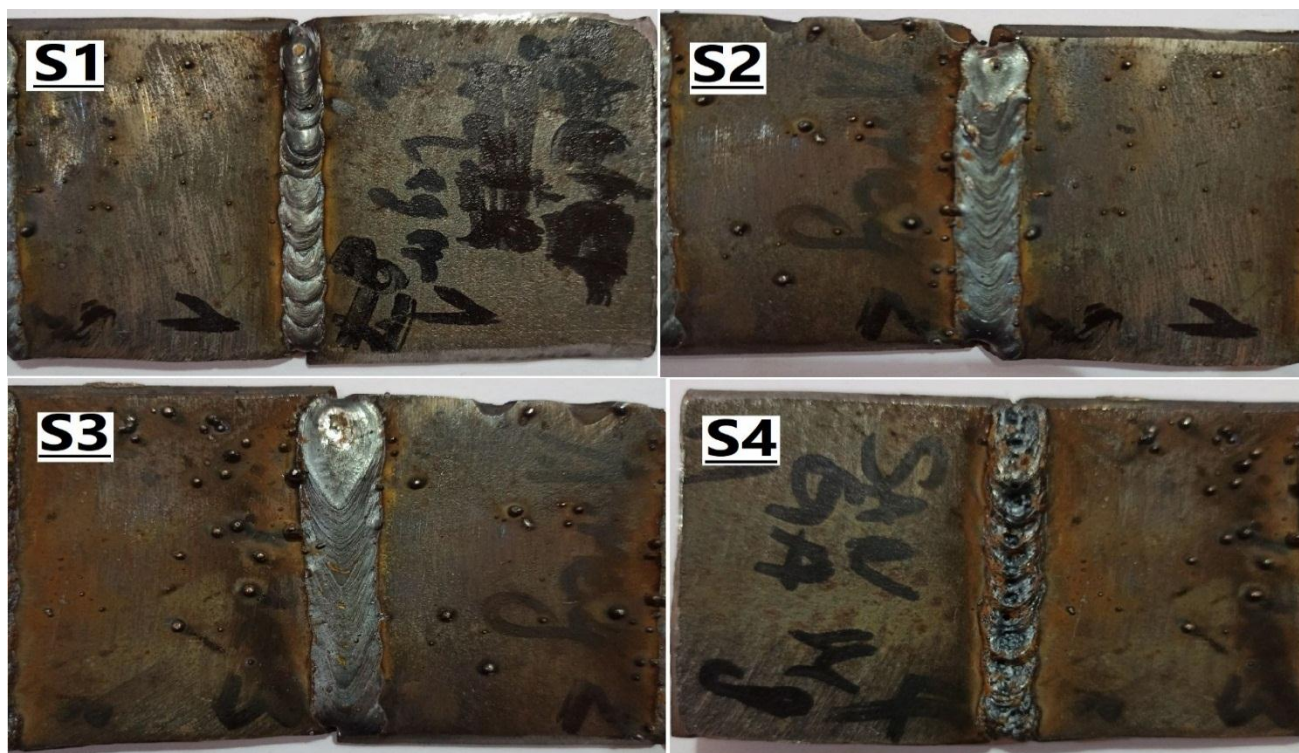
Éprouvettes N°2 après soudage.
